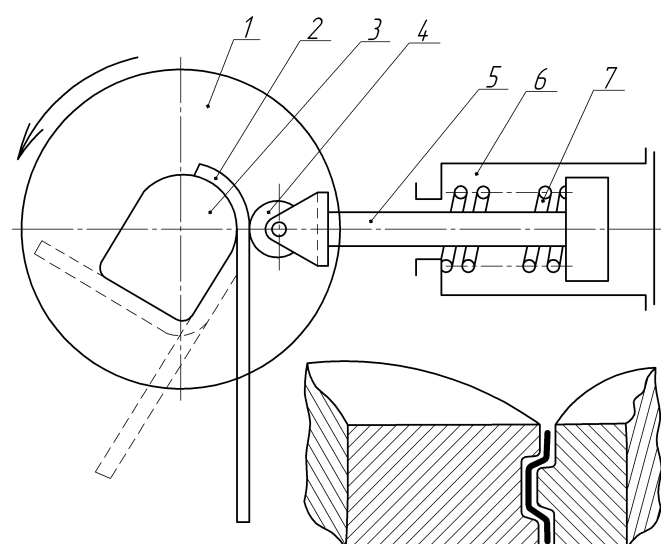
Схема машини з поворотним столом для згинання профільних заготовок
